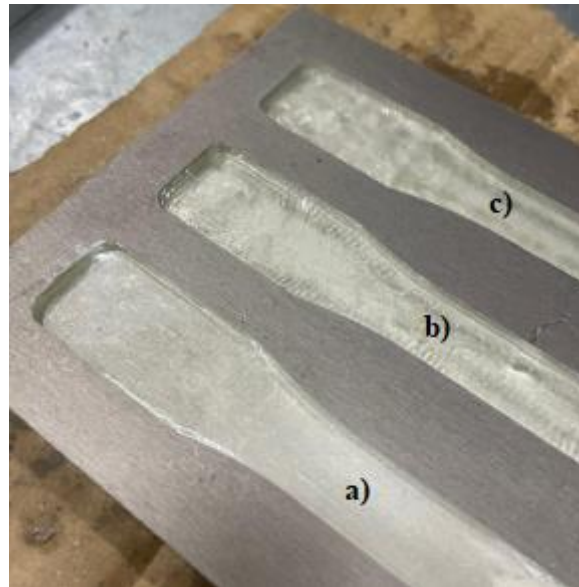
Corpos de prova em molde de metal: (a) completamente curado; (b) e (c) cura não realizada
